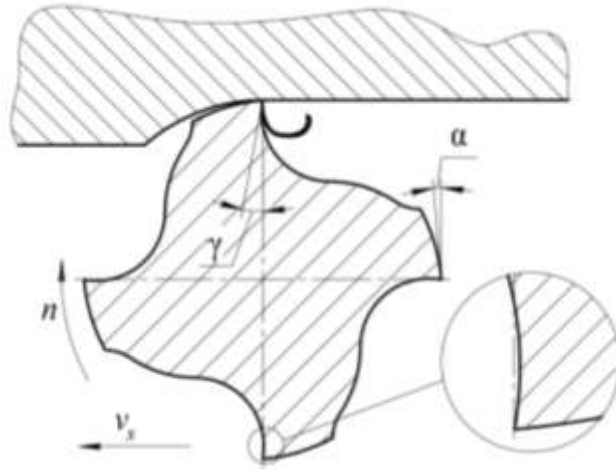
Робота ріжучого клина при фрезеруванні
